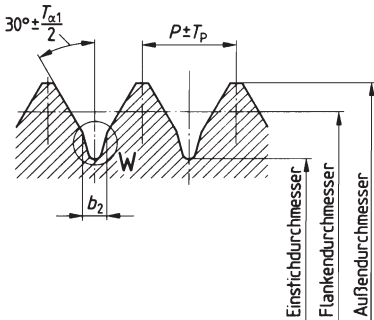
Profil mit voller Flanke (Bolzensgewinde)
